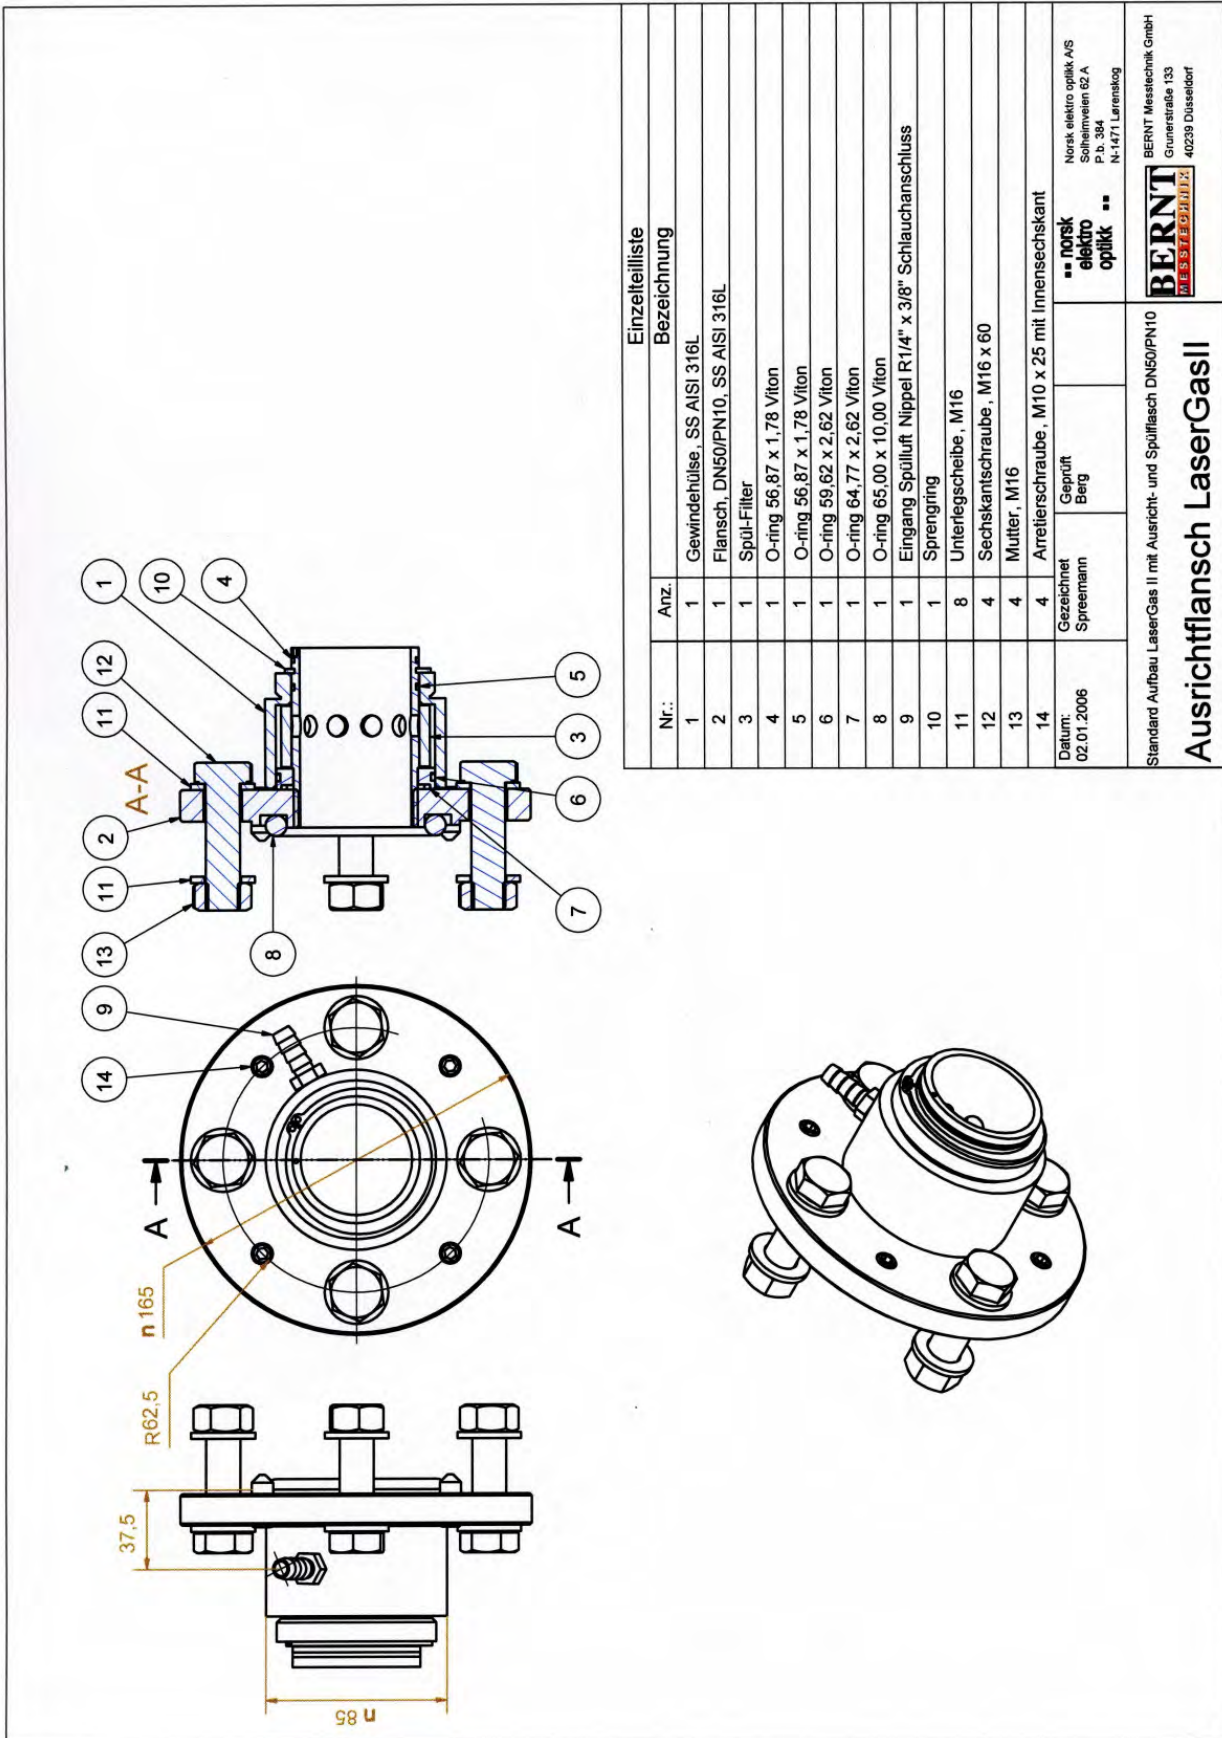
Konstruktionszeichnung des Ausrichtflansches
